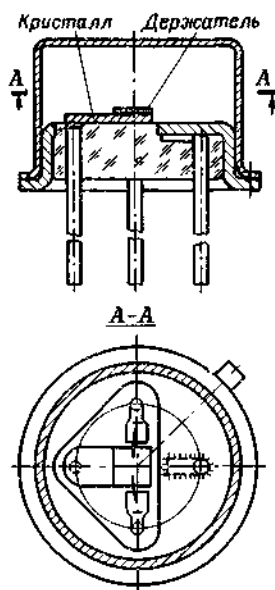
Конструкция корпуса КТ-22. Вариант для монтажа кристалла на вывод корпуса.
